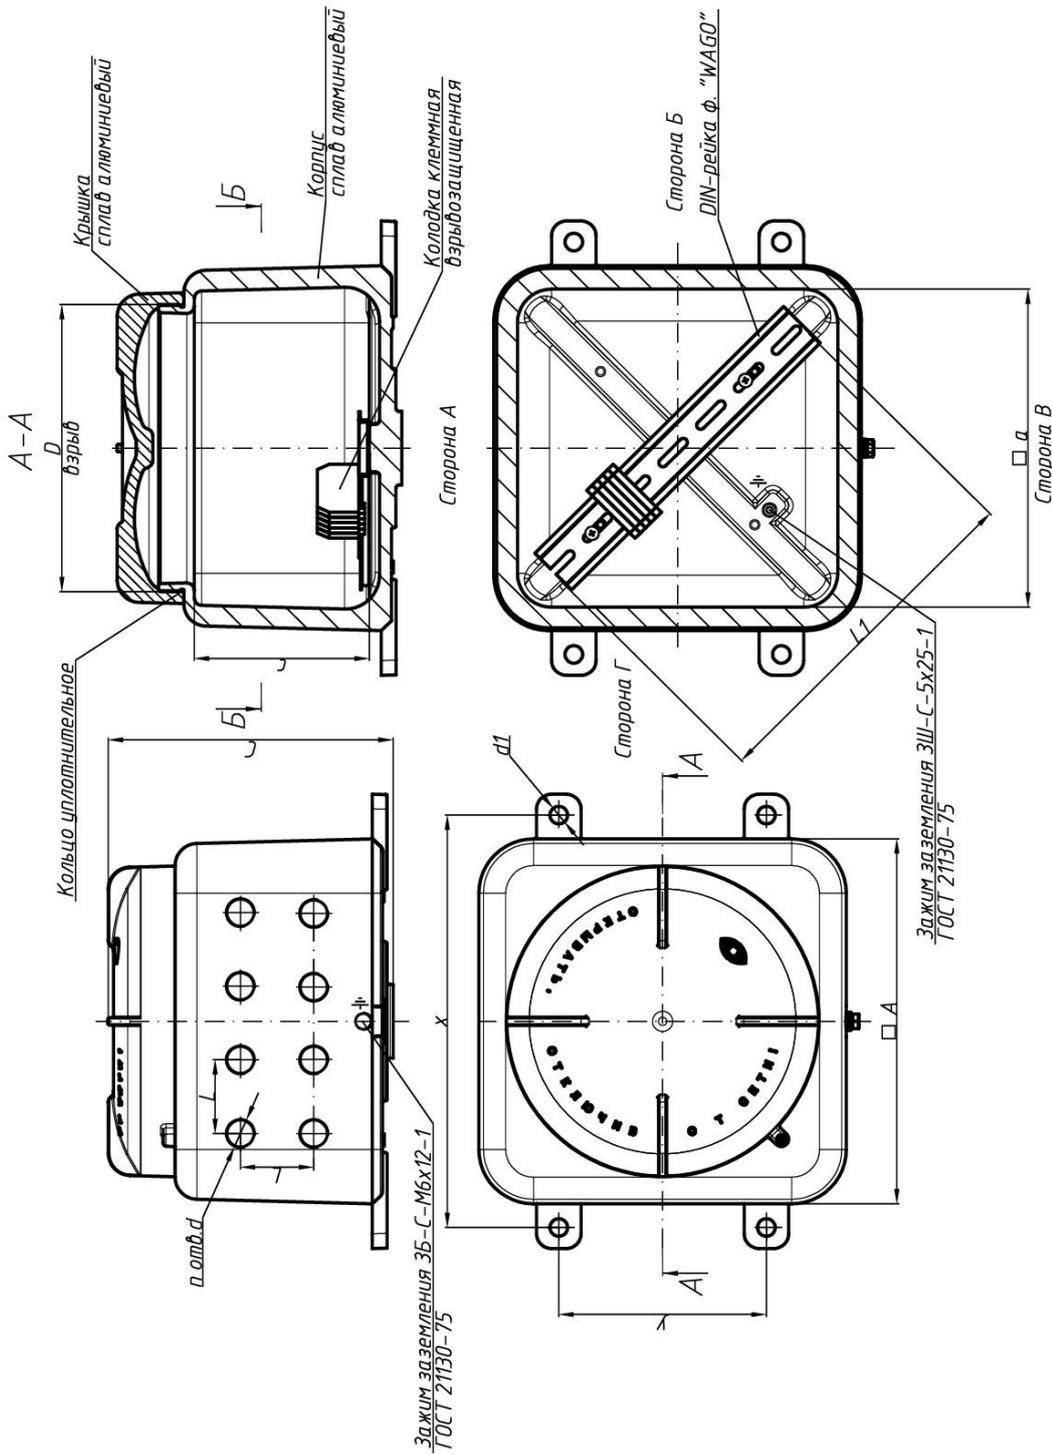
Габаритные и установочные размеры коробок ЕхКСУВ-ВОС с элементами взрывозащиты. См. также таблицы ниже.
